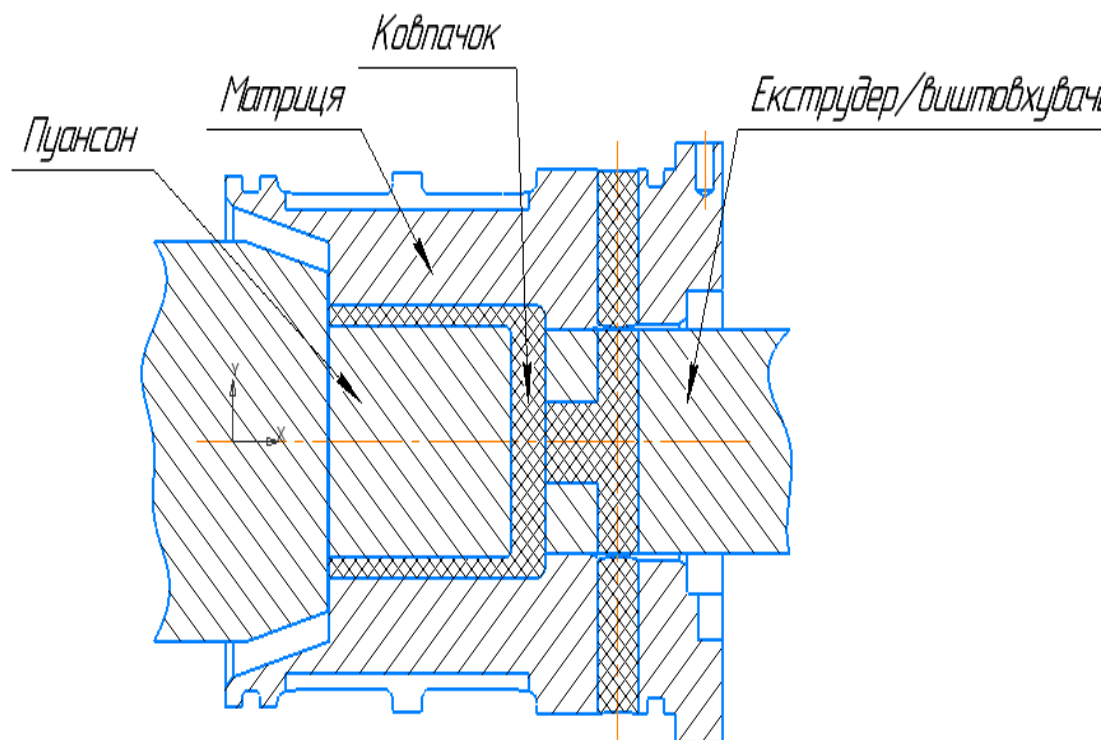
Ескіз виготовлення деталі «Ковпачок»
